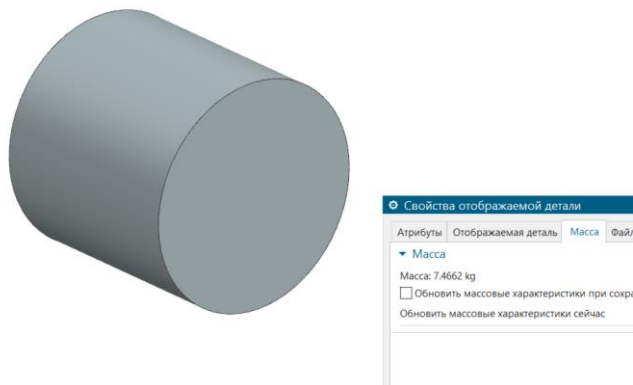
Ескіз заготовки отриманої з прокату
